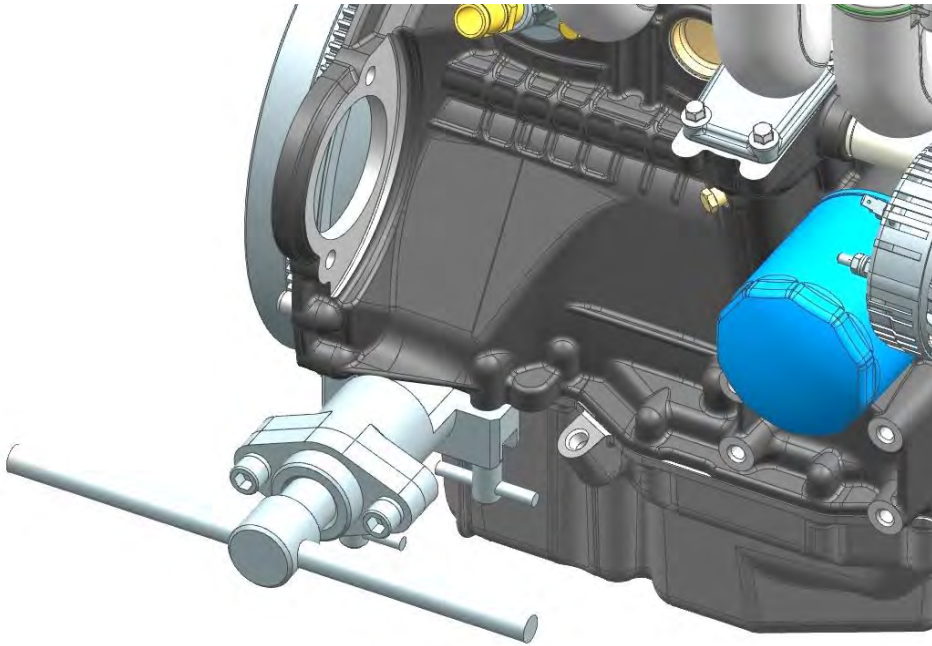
Montage des Werkzeugs ZM 7823-4815 am Motor
